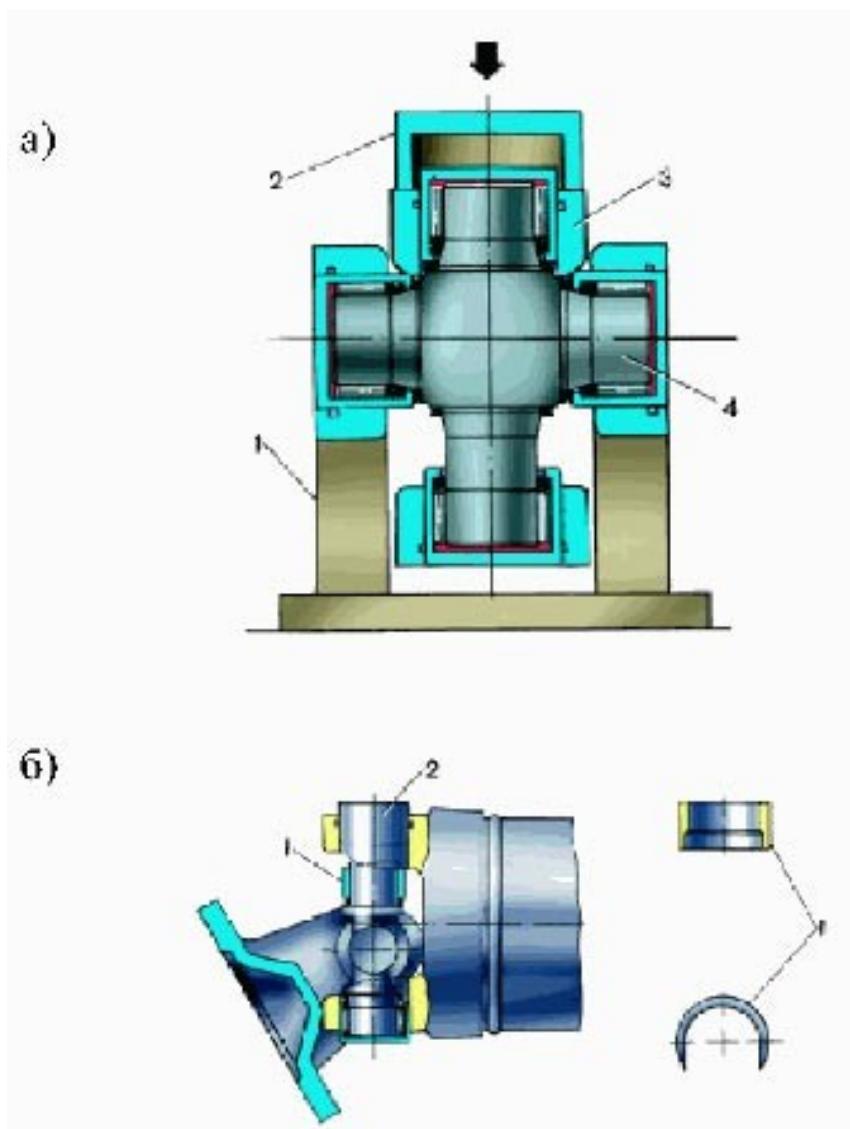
Розбирання карданного шарніра (нова конструкція):
